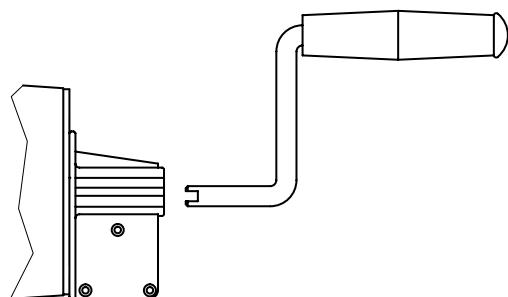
Аварийный ручной привод. Стандартная приводная рукоятка.
